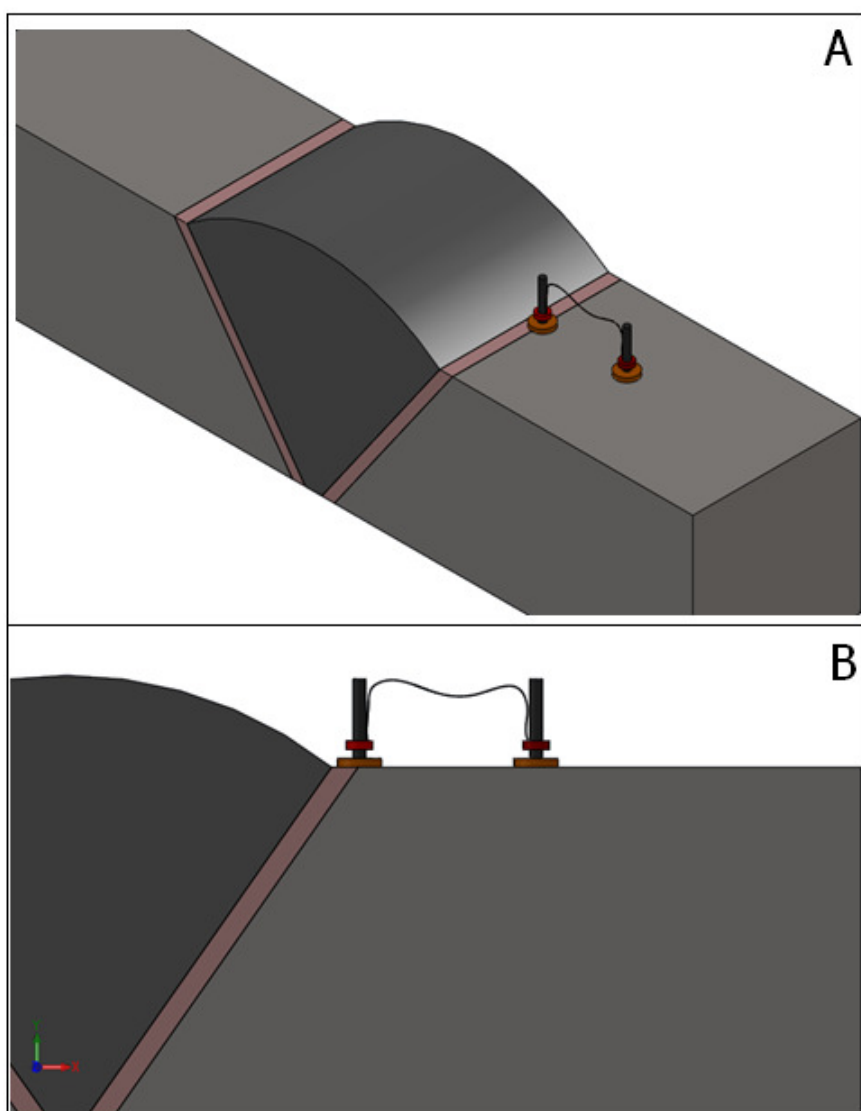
Vistas da configuração da sonda proposta para inspeção de ZTAs de juntas soldadas do aço inoxidável duplex. A: Vista isométrica. B: Vista frontal.
